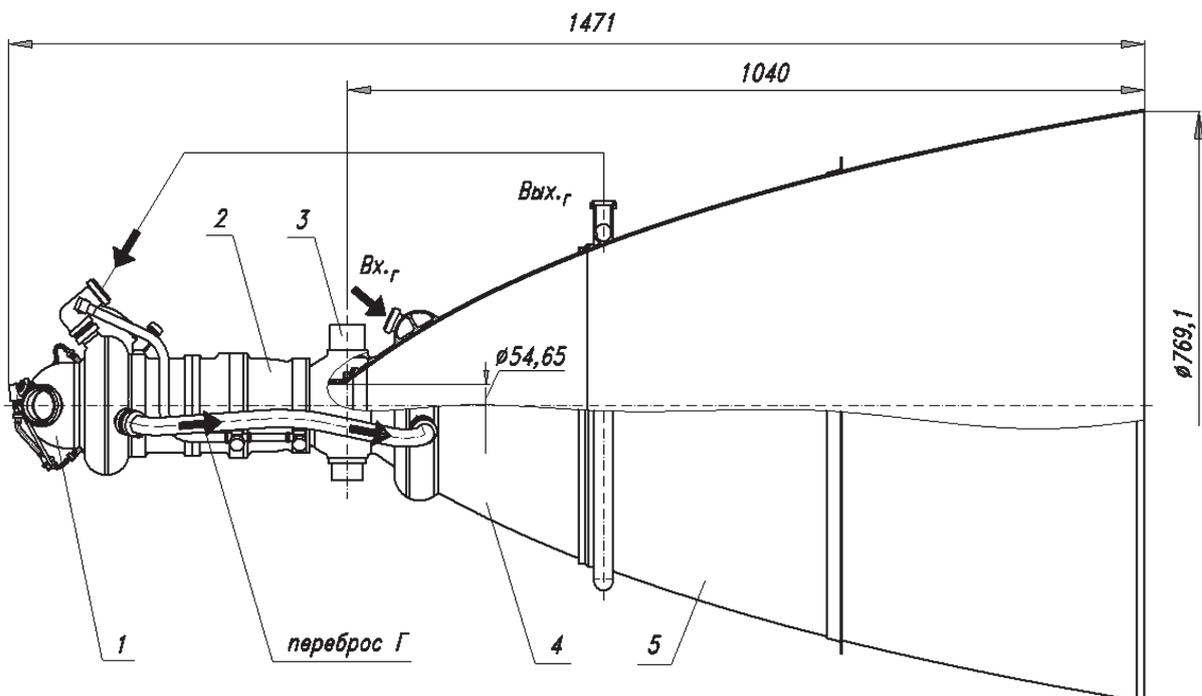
Камера двигателя РД0124: 1 – головка смесительная с газоводом; 2 – блок камеры; 3 – бандаж с цапфами; 4 – сопло верхнее; 5 – сопло нижнее
